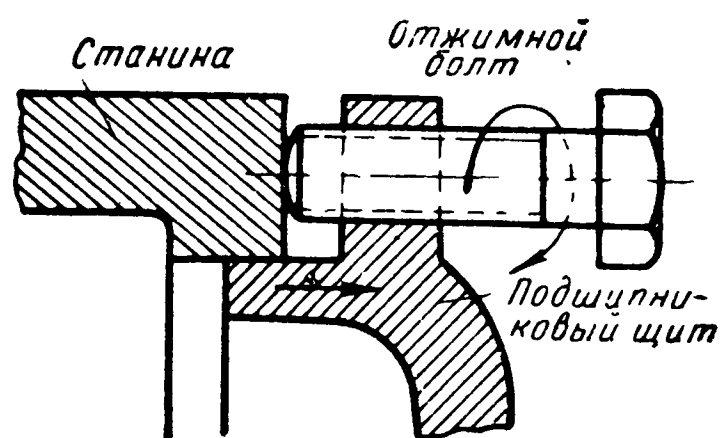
Съем подшипникового щита при помощи отжимного болта
